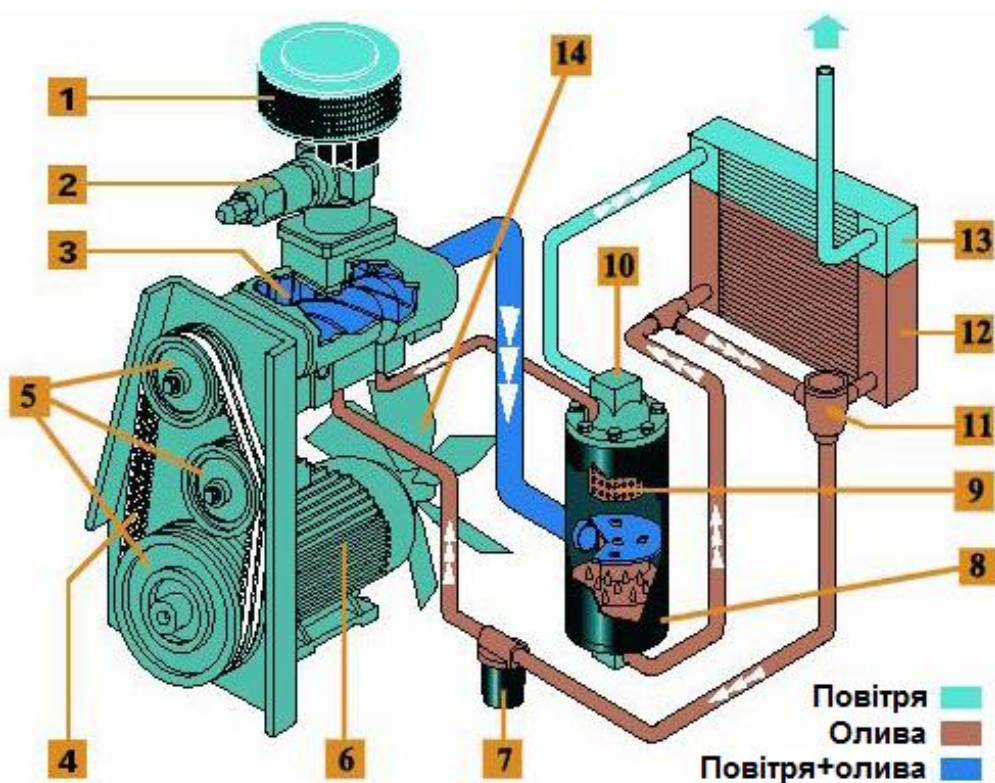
Схема роботи гвинтового (роторного) компресора:
